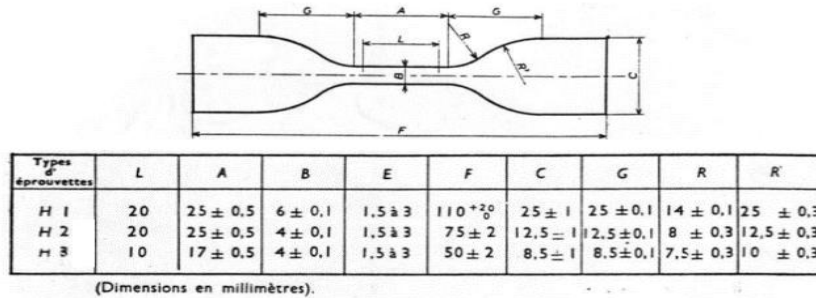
Dimensions des éprouvettes de traction de type H1, H2 et H3
